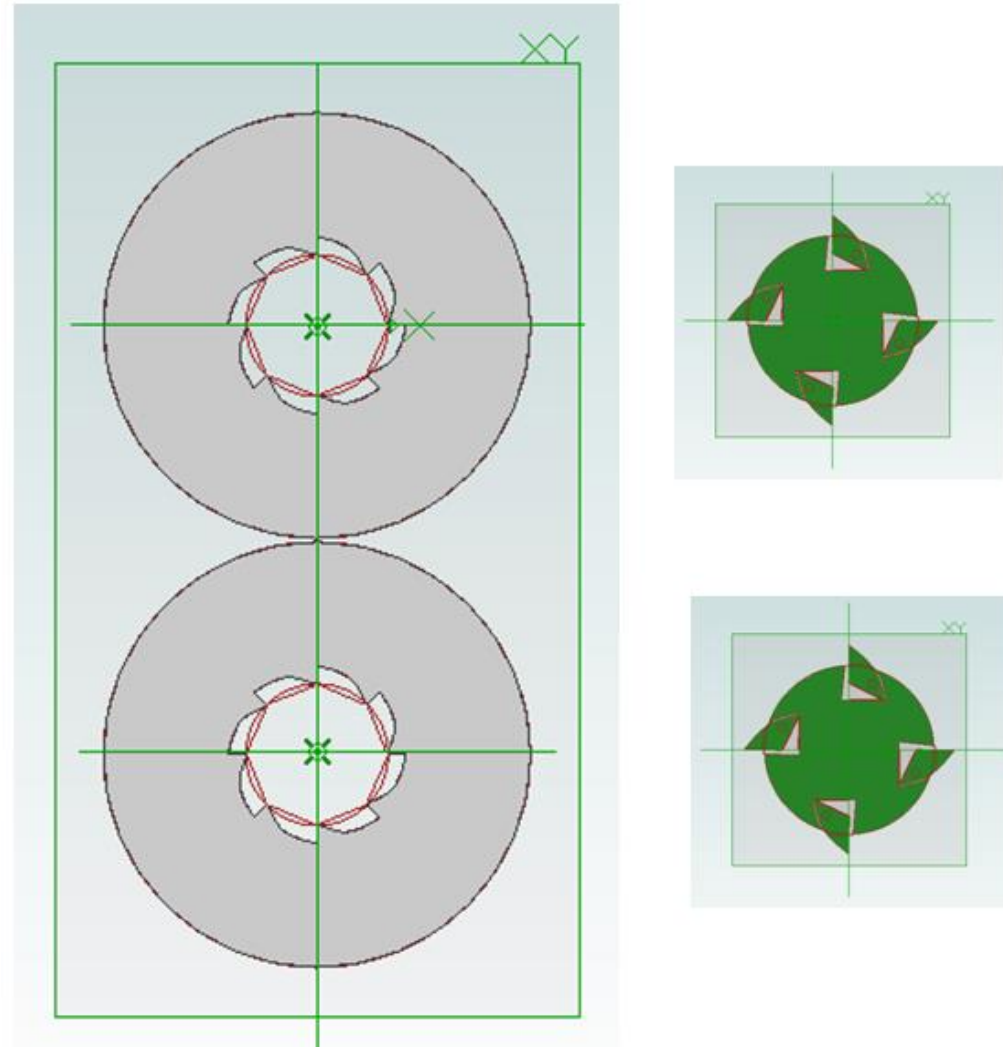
Rodas dentadas com os socacos e detalhe dos dentes dos veios/Inner diameter of the main gears and the shaft locking detail.
